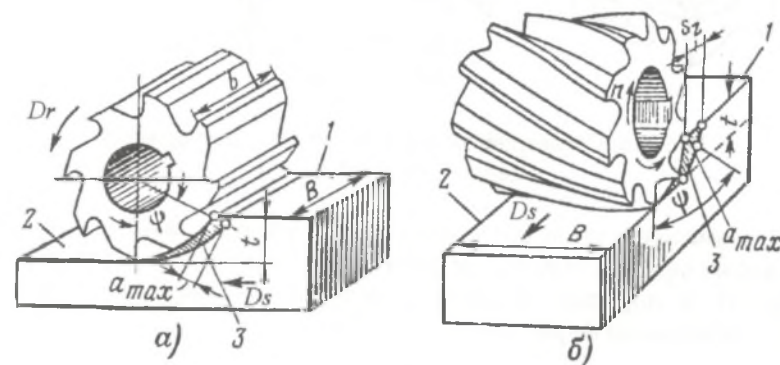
Схема работы цилиндрической фрезы: а – с прямыми зубьями; б – с винтовыми зубьями; 1 – обрабатываемая поверхность; 2 – обработанная поверхность; 3 – поверхность резания
